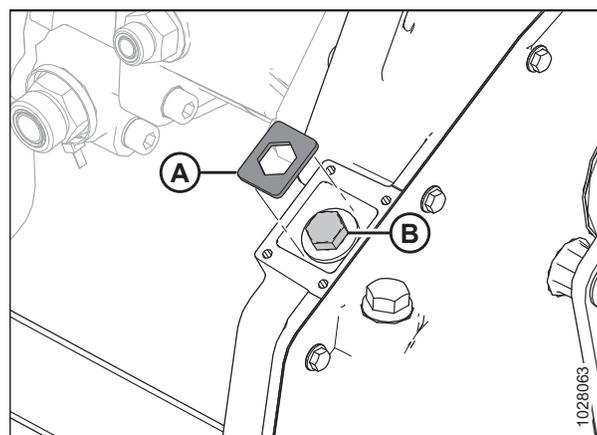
Hauptgetriebe mit Kettenspanner
